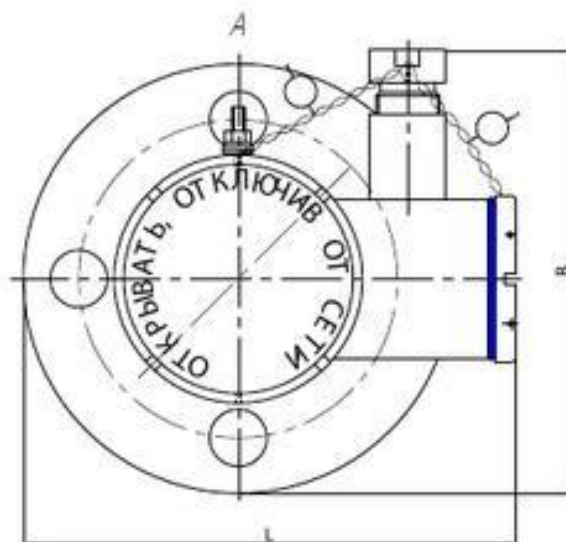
Габаритные и присоединительные размеры ПП МГДУ ЛП.
